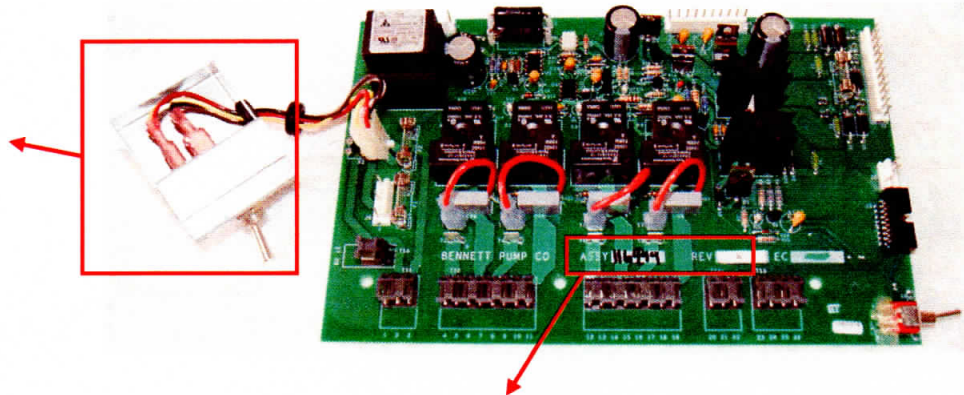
Detalle de etiqueta que identifica el número de parte de la tarjeta Power Distribution Board Assembly.
